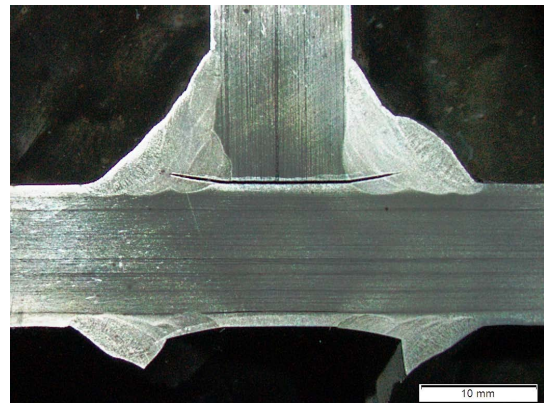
Probe G03-04, Schweißnaht FAT 90, Riss an der Schweißnaht, Nahtanstiegswinkel zu groß
